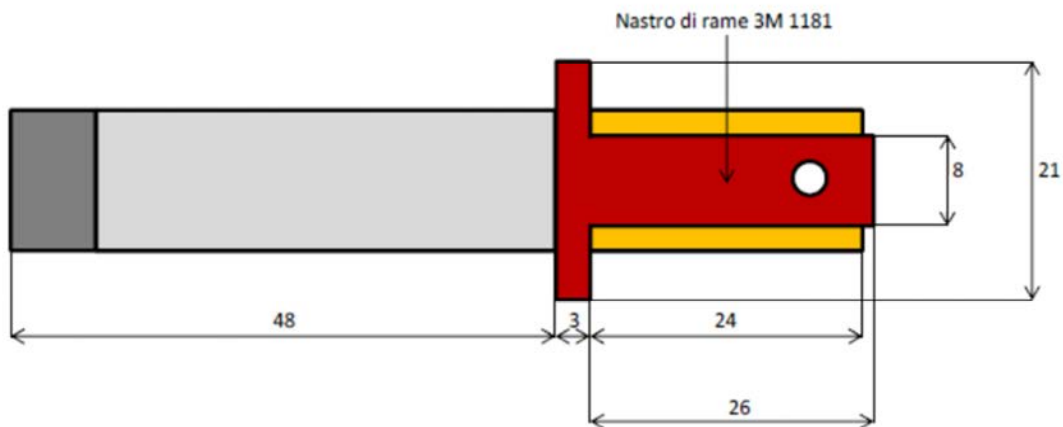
Applicazione del nastro di rame 3M 1181 alla barretta di alluminio.
